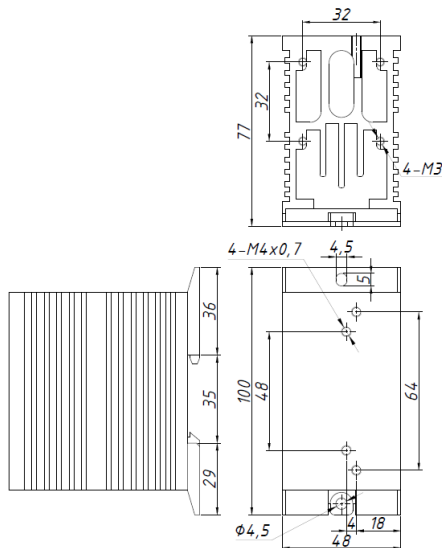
габаритные и установочные размеры радиатора РТР052
